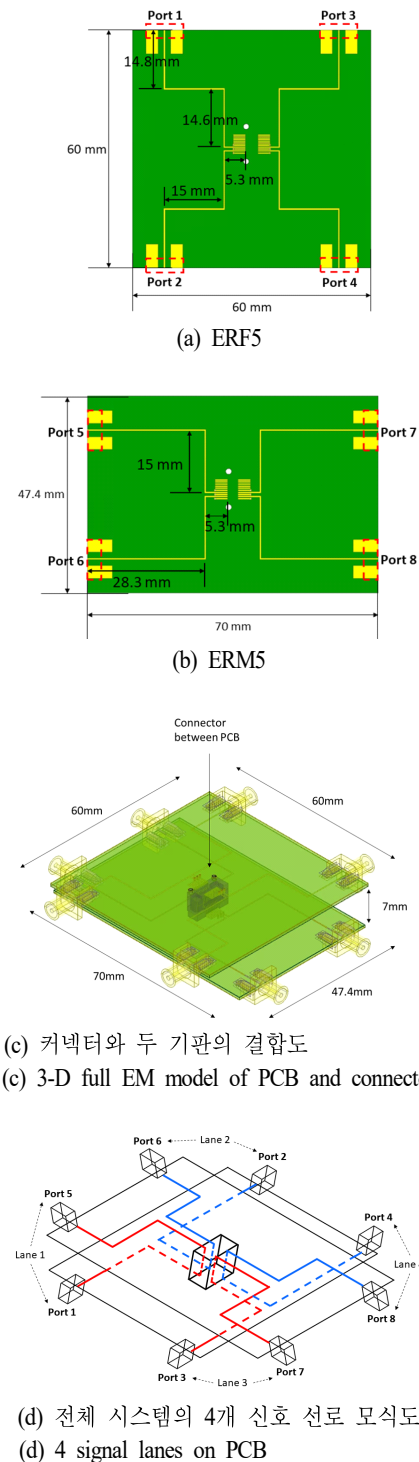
Test fixture 기판 및 커넥터와의 결합 형태
